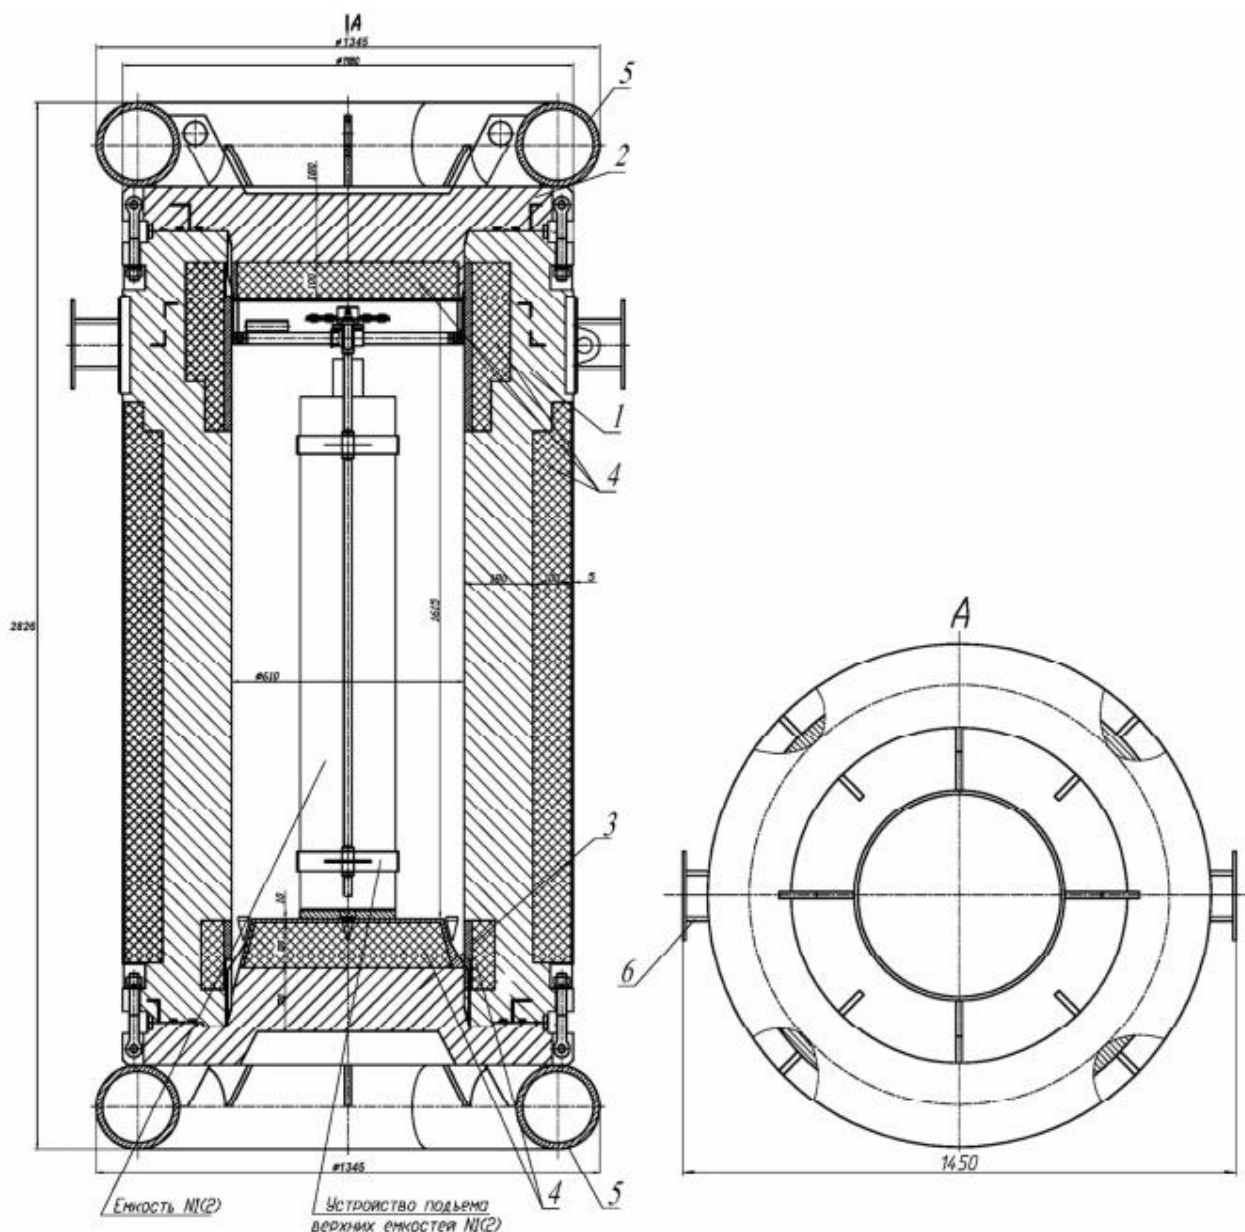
,б. Разрез ТУК: 1 – корпус; 2 – крышка верхняя; 3 – крышка нижняя; 4 – защита нейтронная; 5 – амортизатор; 6 – цапфа
